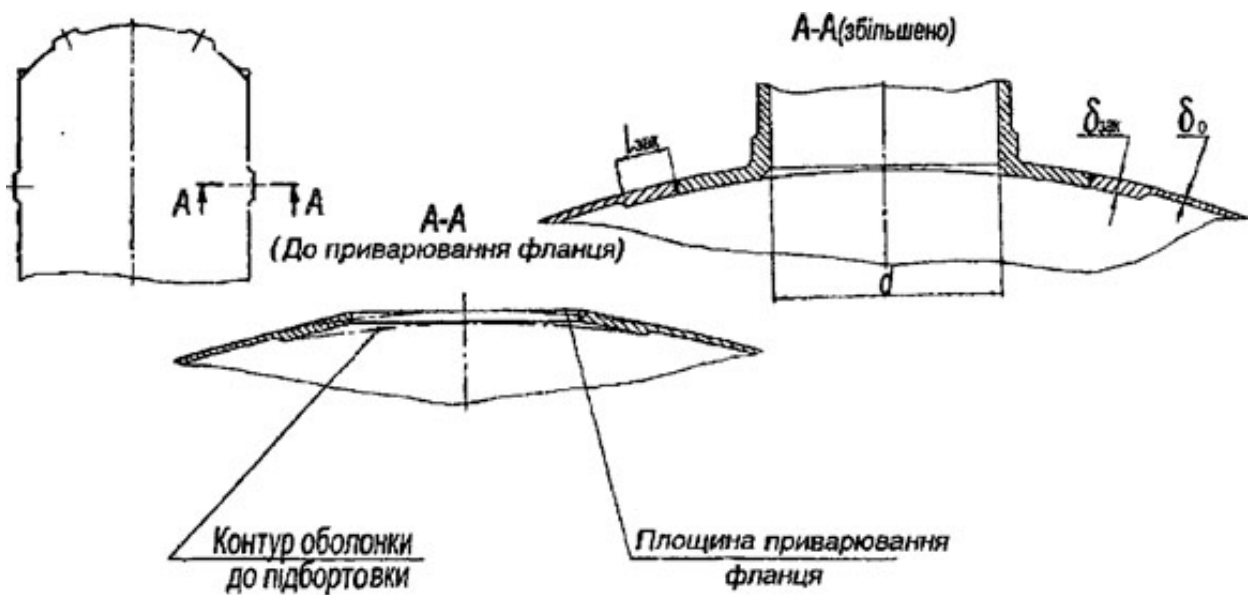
Застосування підбортовки для приварювання фланця на циліндрі бака
